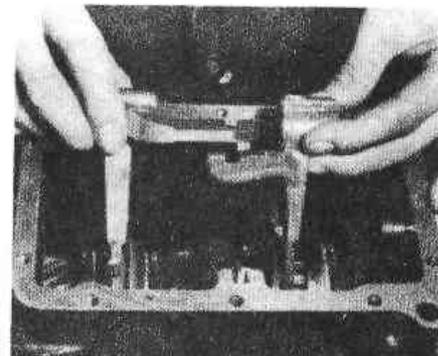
Вилки механизма включения передач коробки типа С (Разд. 7)
